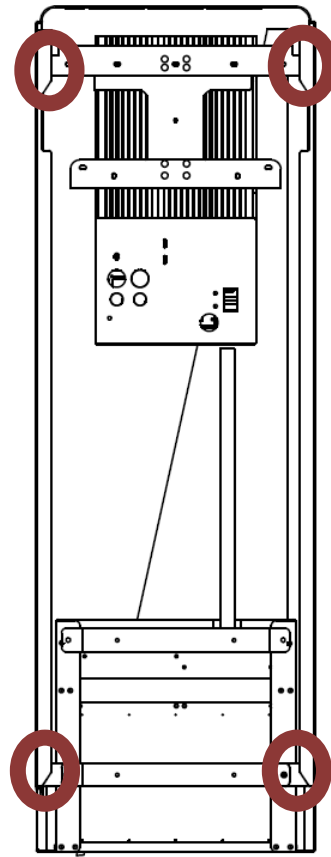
Vista de la tapa posterior, bridas cubiertas.
